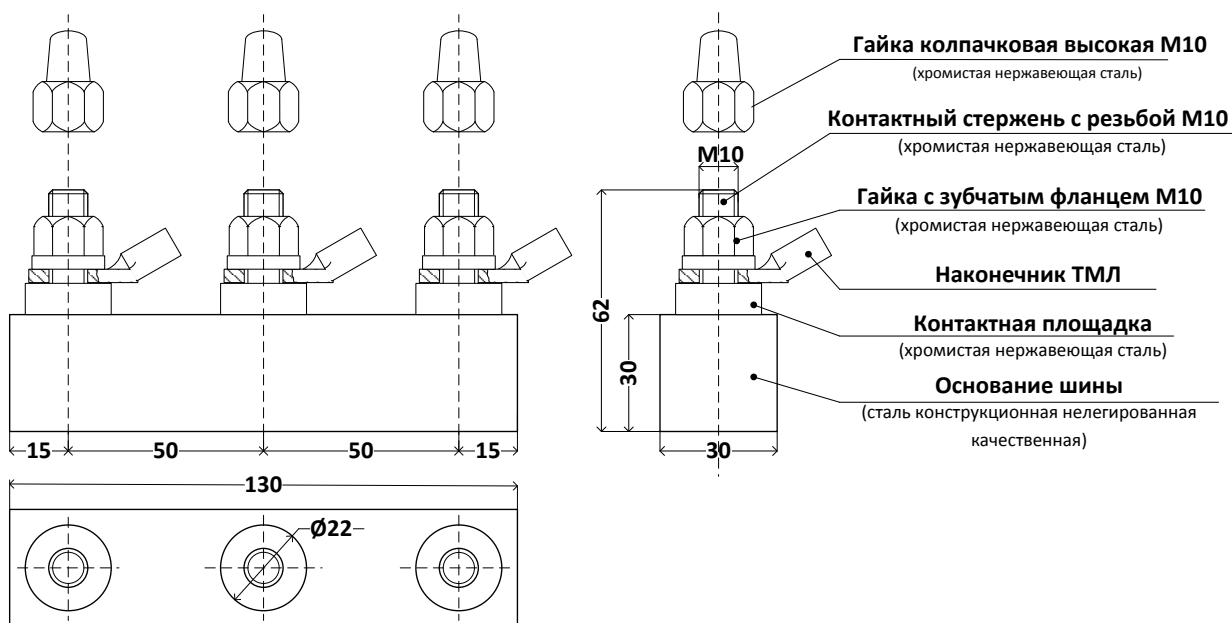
Габаритные размеры и последовательность сборки контактного соединения шины ШЗ-МК-3х10
